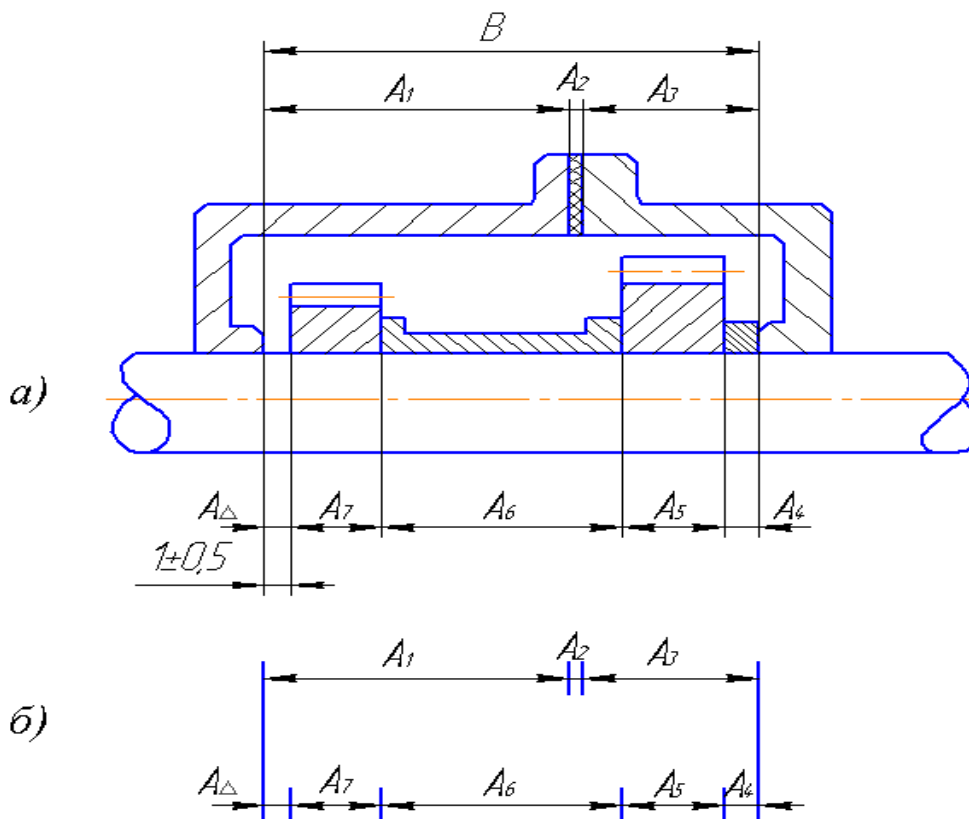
Схема простановки размеров (а) и построения размерной цепи (б) сборочного узла
